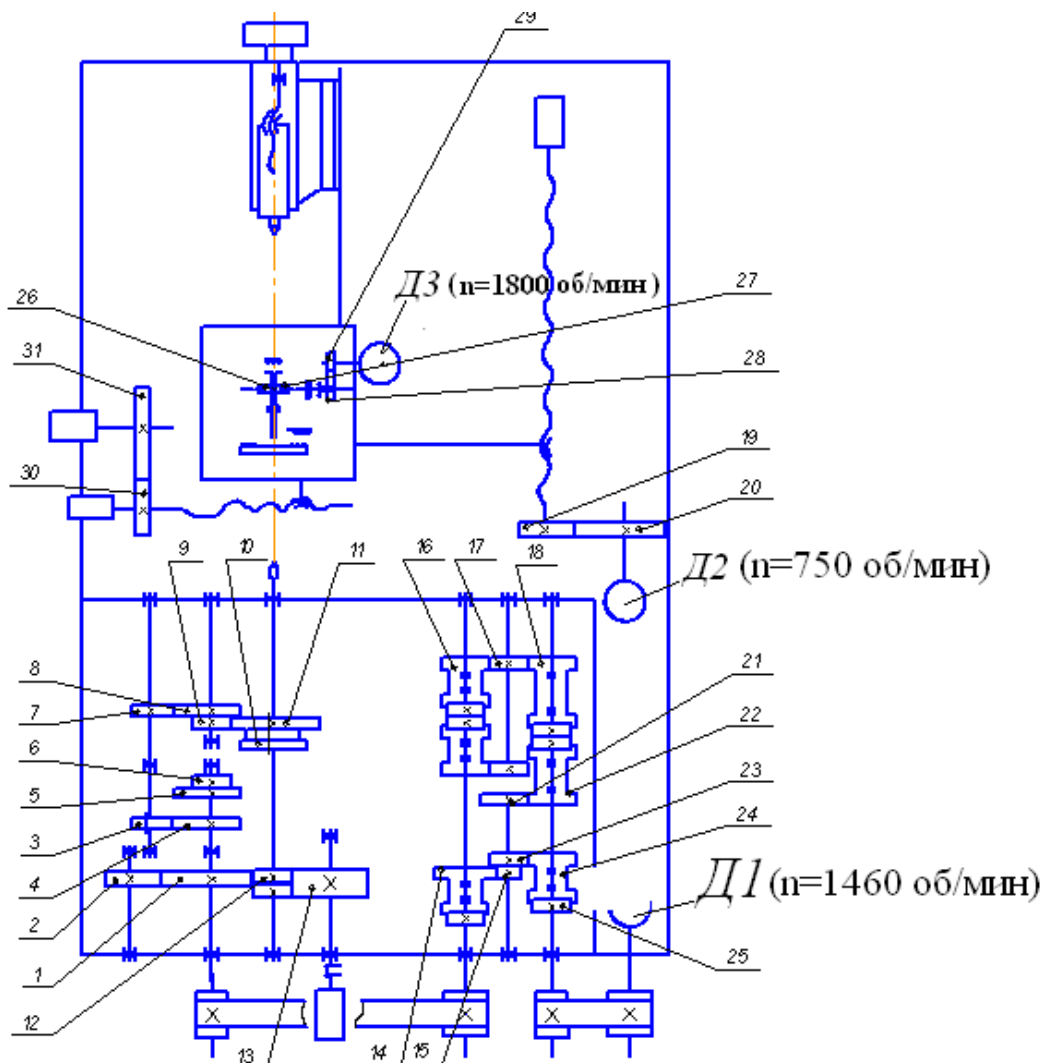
Кинематическая схема токарного станка 16К20Т1
